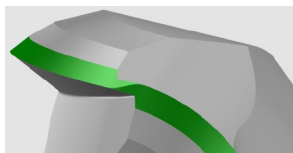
Zentrum des Vollradiusfräasers mit einer S-förmigen Querschnitte
